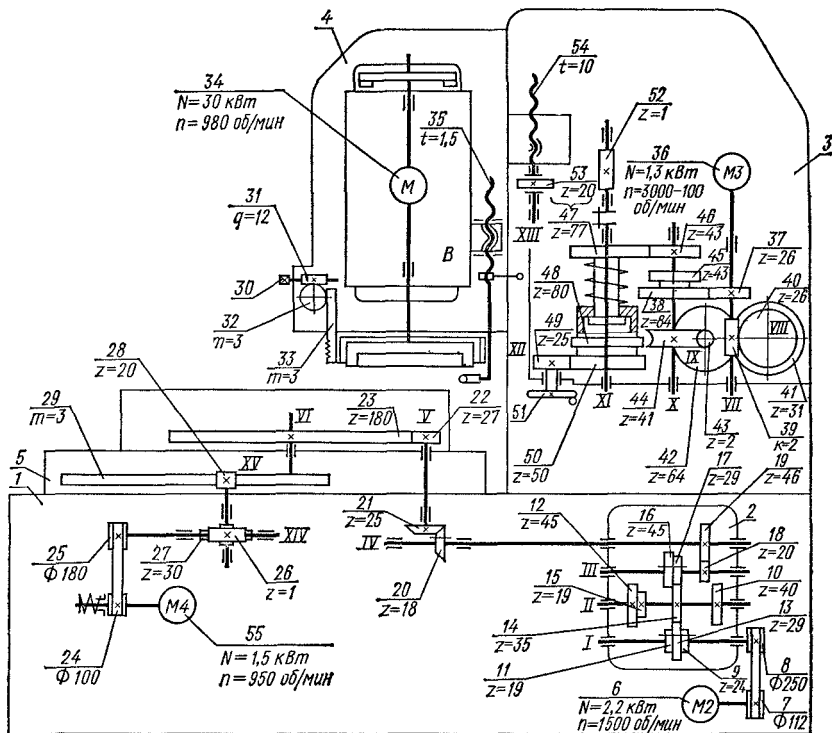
Кинематическая схема плоскошлифовального станка мод. 3Д756
